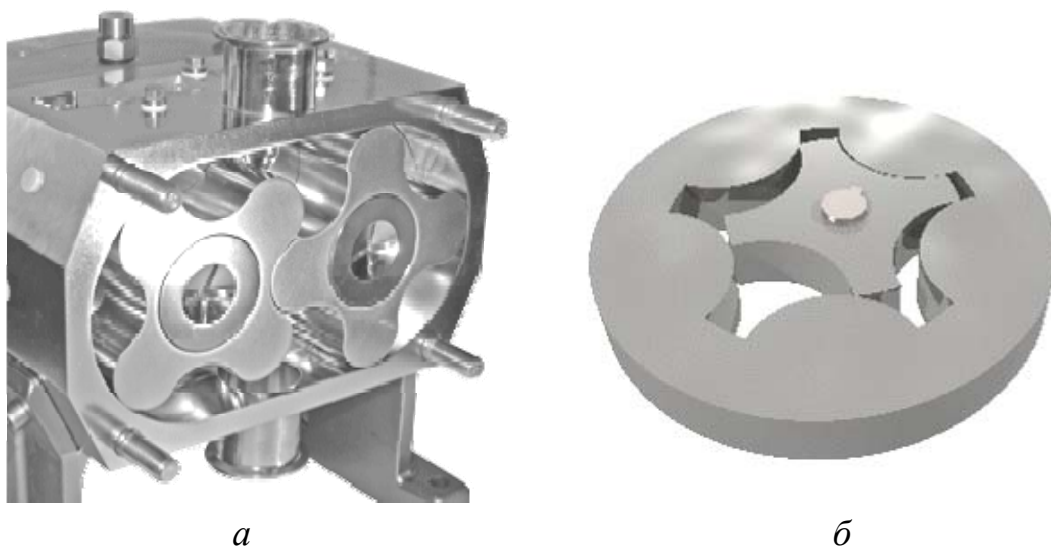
Кулачковый насос в разрезе (а) и колесо шестерёнчатого героторного насоса (б)
